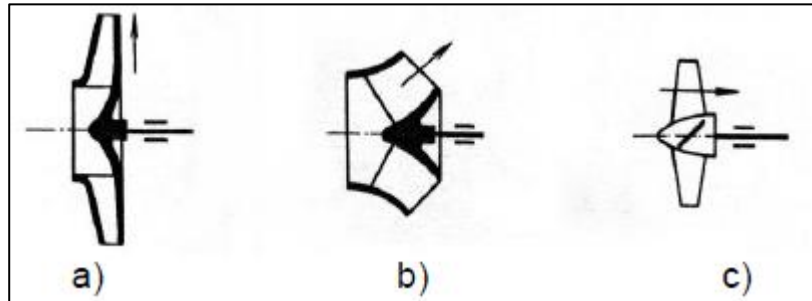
Esquemas de rotores: a) radial b) misto c) axial [28].
